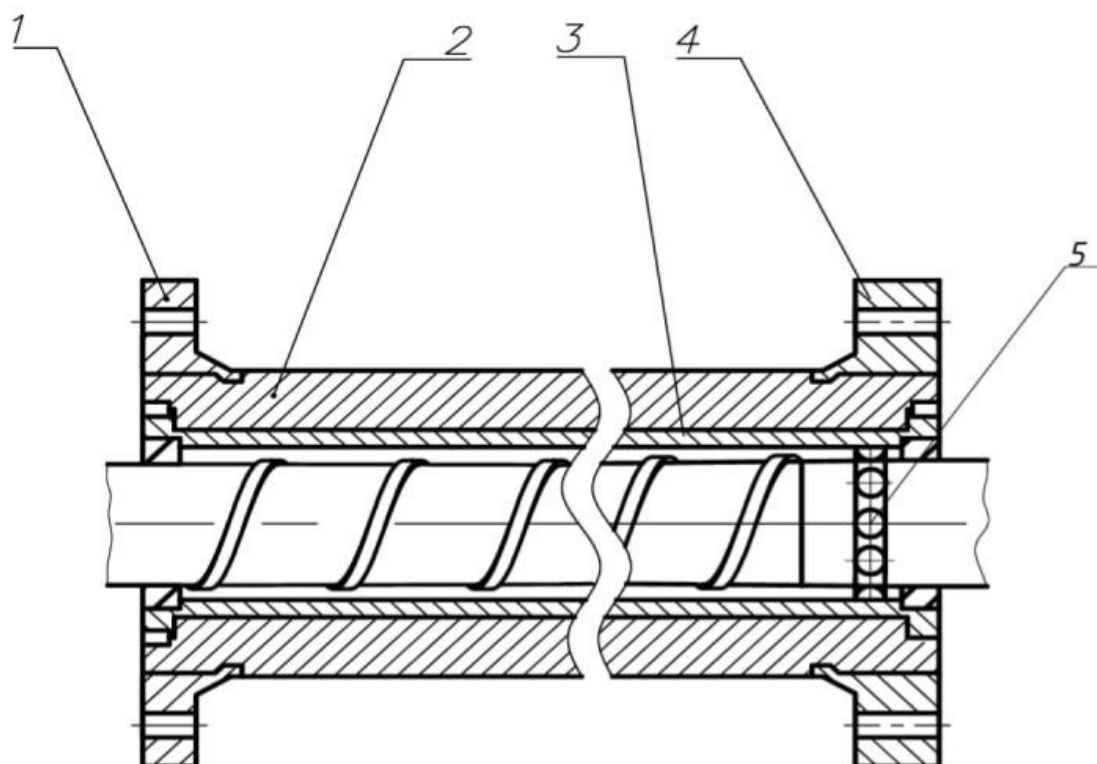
Вигляд модернізованої конструкції корпусу [5]: 1 – фланець правий; 2 – корпус; 3 – гільза; 4 – фланець лівий; 5 – тіла обертання
